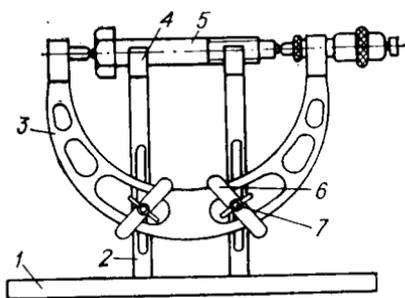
Приспособление для определения величины остаточного удлинения шатунных болтов:
